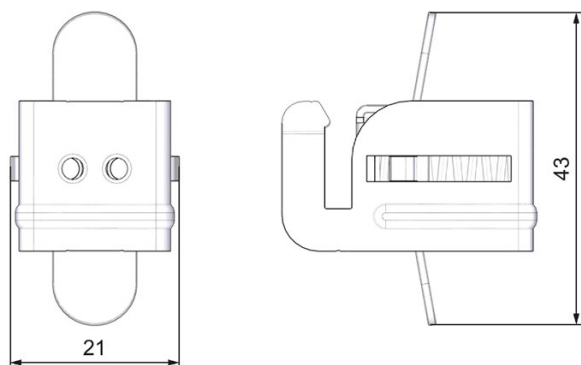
Maßbild Schirmklemme für 25 mm-Module
